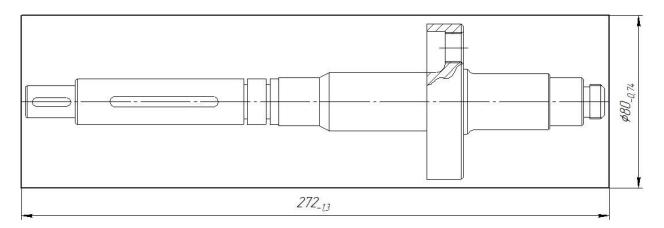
Заготовка детали «Фланцевый вал» из проката Рассчитаем массу проектной заготовки:
